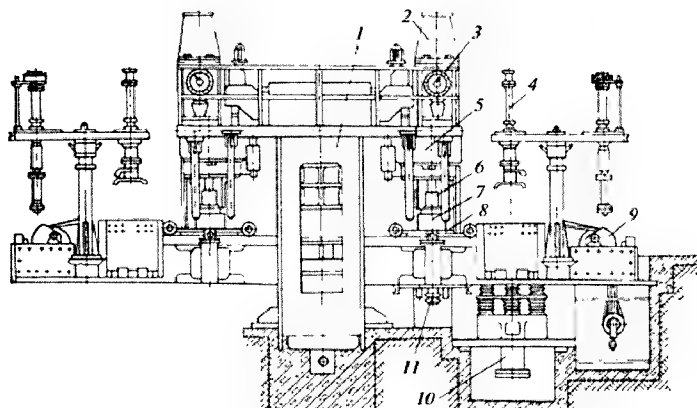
Автоматический формовочный агрегат АФА-9:
